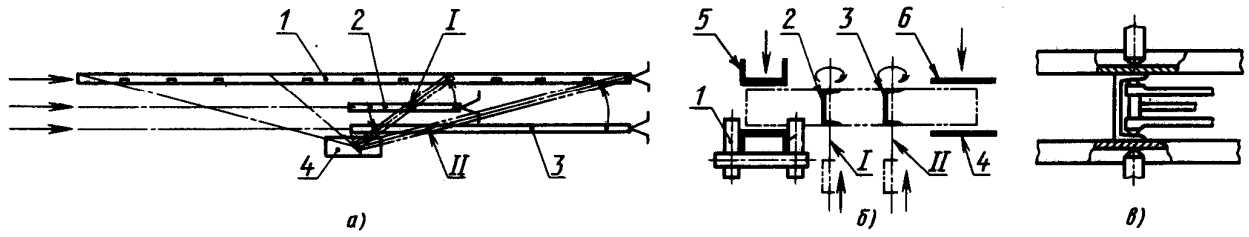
Схема сборки и сварки стропильной фермы
